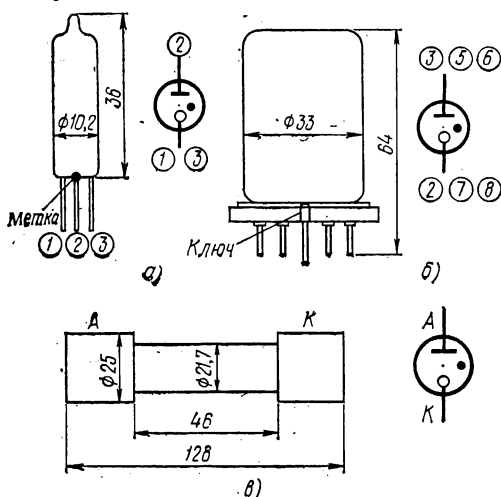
Габаритные чертежи и цоколевка стабилитронов:
